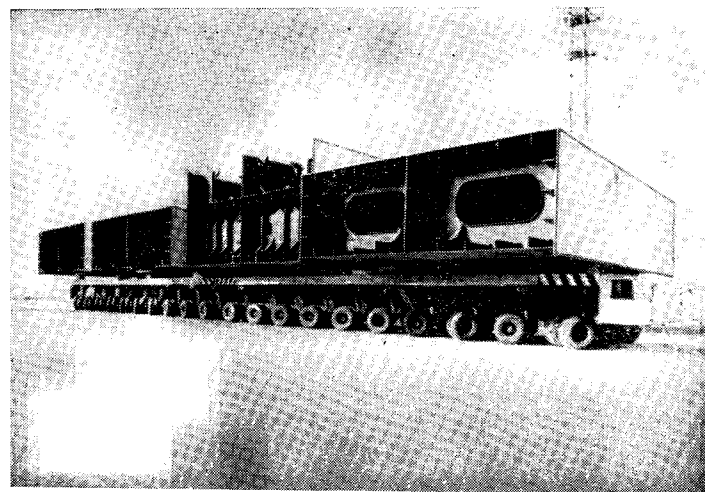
Тяжеловесная платформа на колесном ходу для перевозки блоков, снабженная гидравлическими домкратами. Платформа въезжает под блок и загружает его на себя с помощью гидравлических домкратов.
